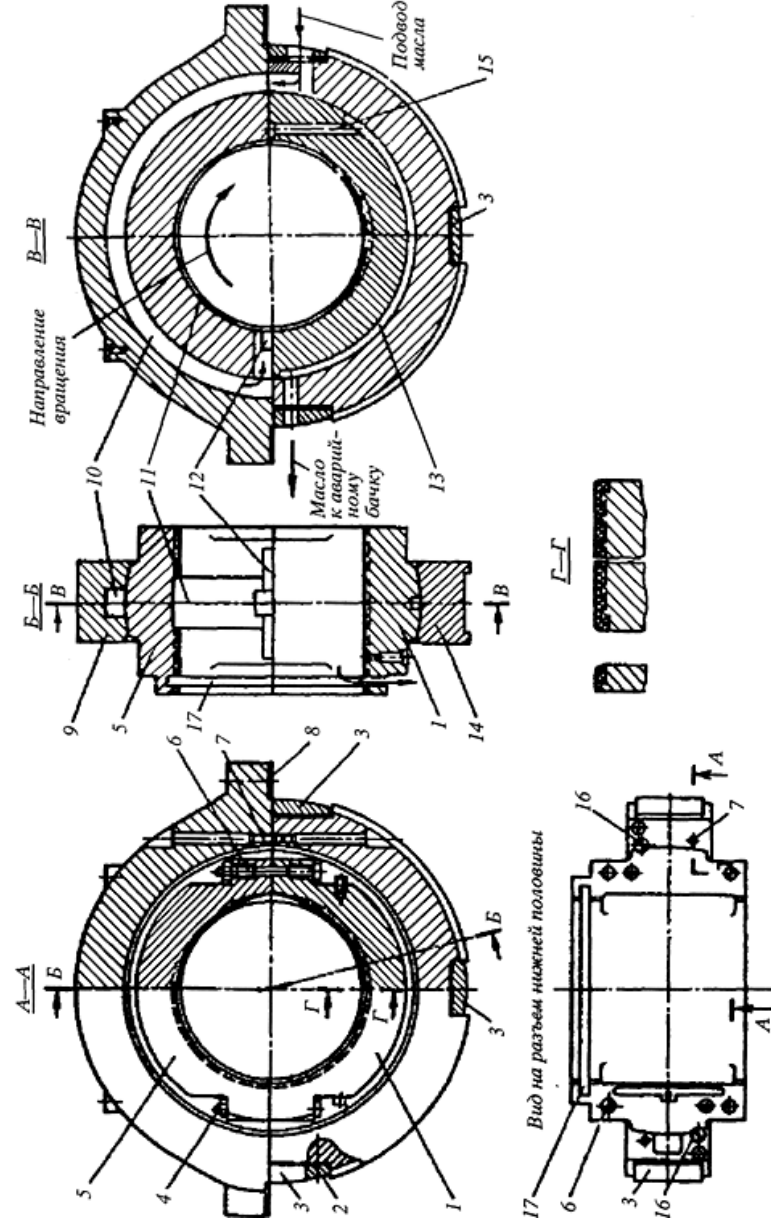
Вкладыш опорного самоустанавливающегося подшипника конструкции ХТЗ: 1, 5 – нижняя и верхняя половины вкладыша; 2 – прокладка; 3 – опорные колодки; 4 – призонные скрепляющие болты вкладыша; 6 – скрепляющие болты вкладыша; 7 – установочные штифты обоймы; 8 – прокладка; 9, 14 – верхняя и нижняя половина обоймы; 10 – канал в сфере вкладыша для подачи масла; 11 – маслораздаточная канавка; 12 – маслораздаточный карман; 13, 15 – каналы подачи масла к аварийной емкости и аварийной подачи масла; 16 – стопорные винты; 17 – маслославливающая канавка
